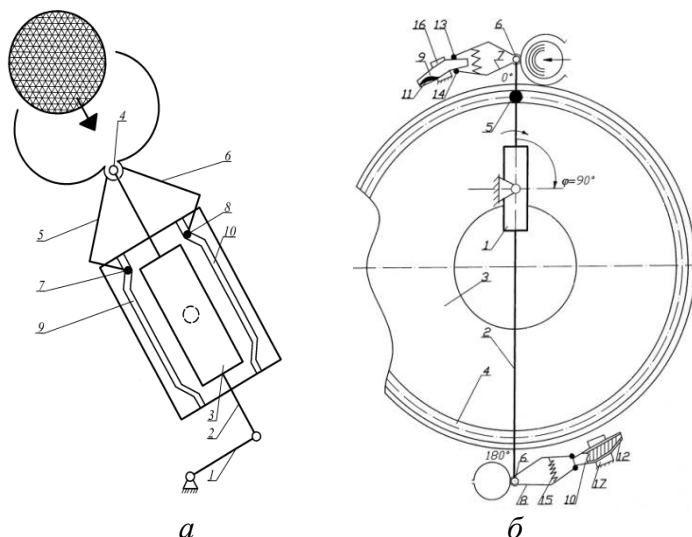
Кинематические схемы устройств для перемещения изделий [2]
